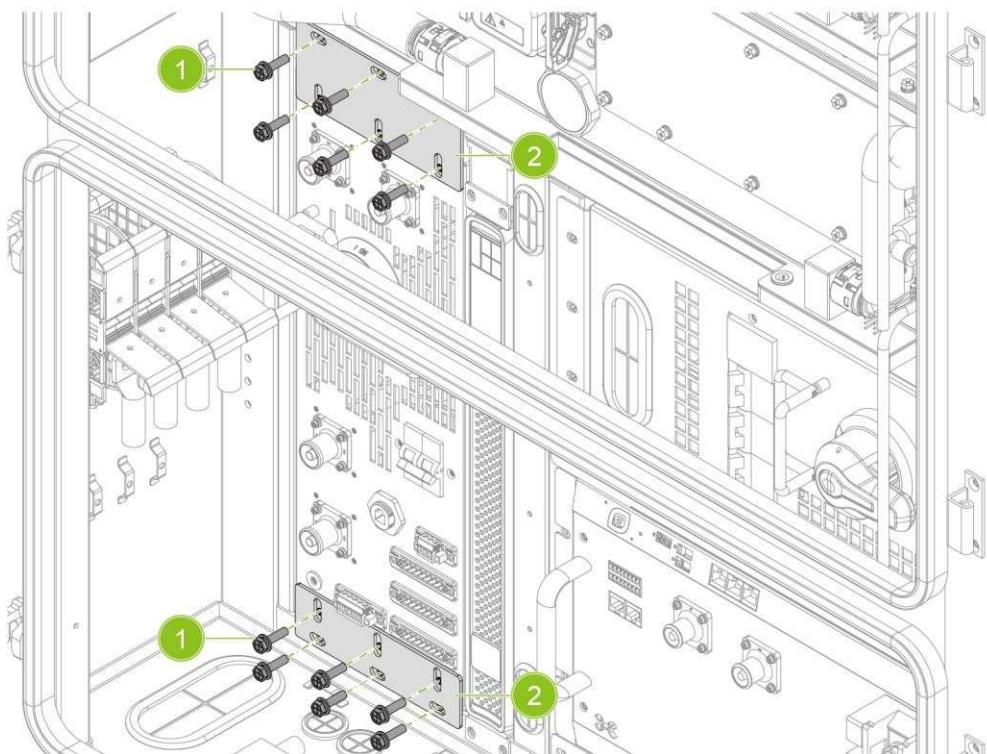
Remova os parafusos combinados e a placa de fixação
